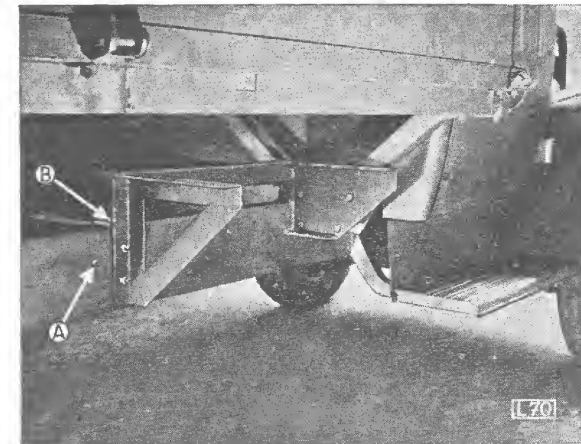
Aufhängung des Gaserzeugers mittels eines am Längsträger befestigten Konsoles
